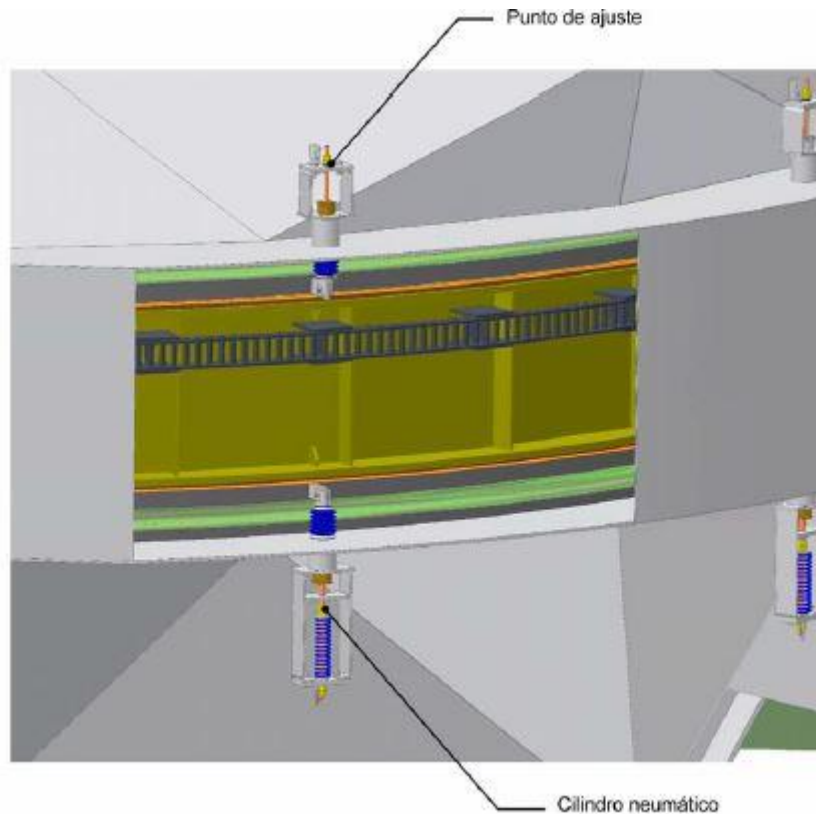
Mecanismos de ajuste de sellado del rotor
